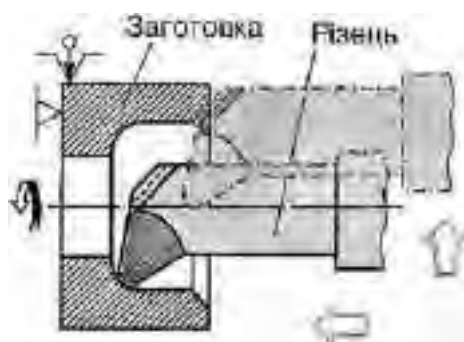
БАГАТОКРОМКОВИЙ РІЗЕЦЬ ДЛЯ РОЗТОЧУВАННЯ ОТВОРУ ТА ЗРІЗУВАННЯ ФАСКИ
